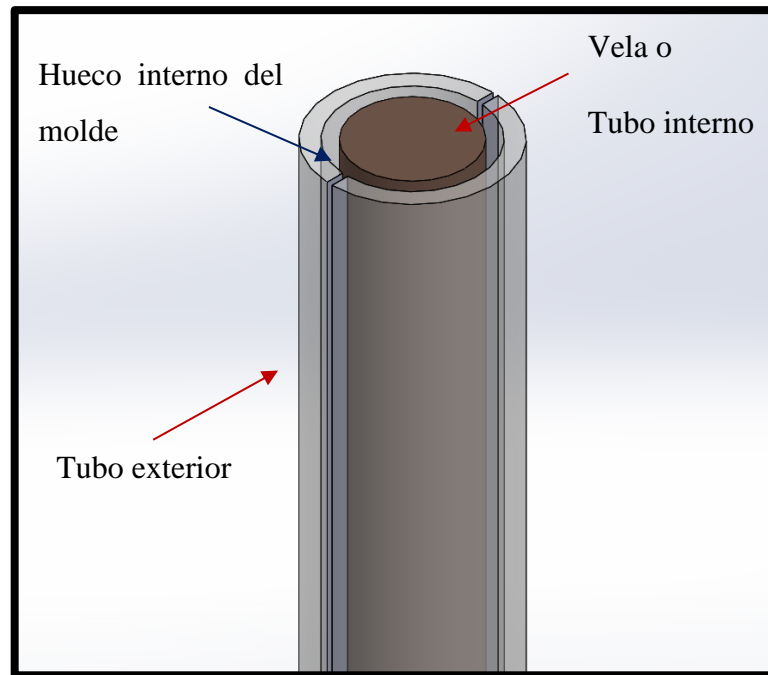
Sólido 3D sobre el esquema del molde desmontable. Fuente: Propia.
